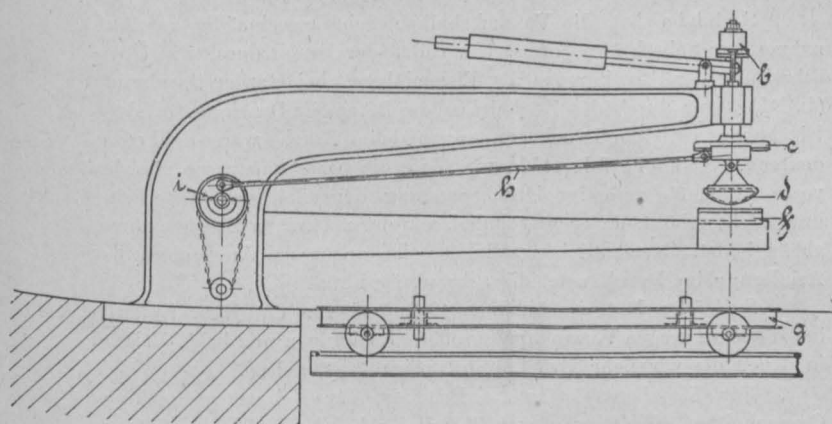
Hydraulischer Schweißapparat Konstruktion Spranger, Seitenansicht
